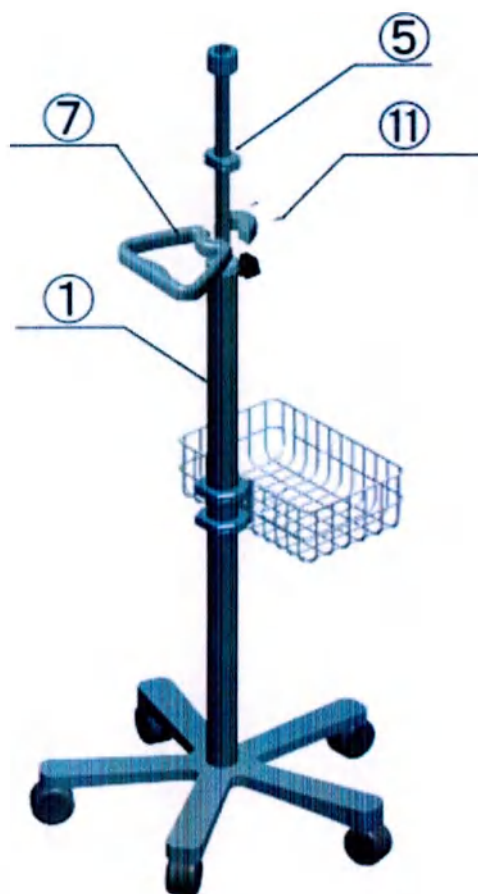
Сборка медицинской стойки Endostand Шаг 4
